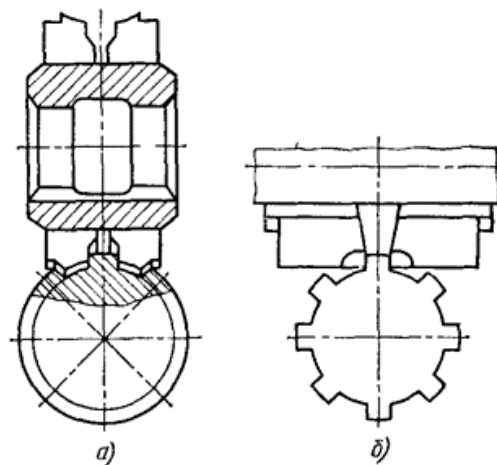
Схема фрезерування шліців фасонними фрезами: а - Попередня обробка; б - чистова обробка бічних поверхонь шліців.
